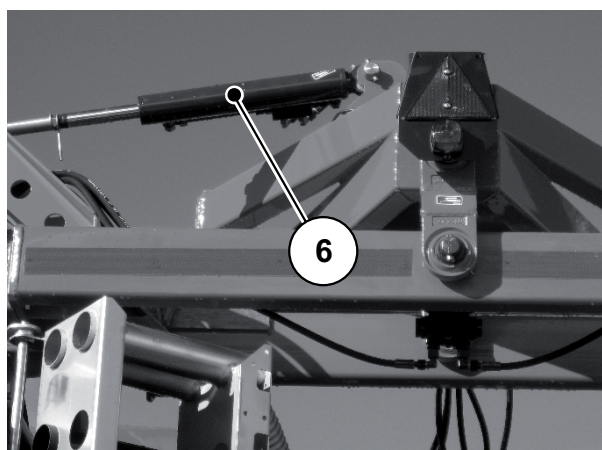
Hydraulický válec rameno vzadu vpravo
